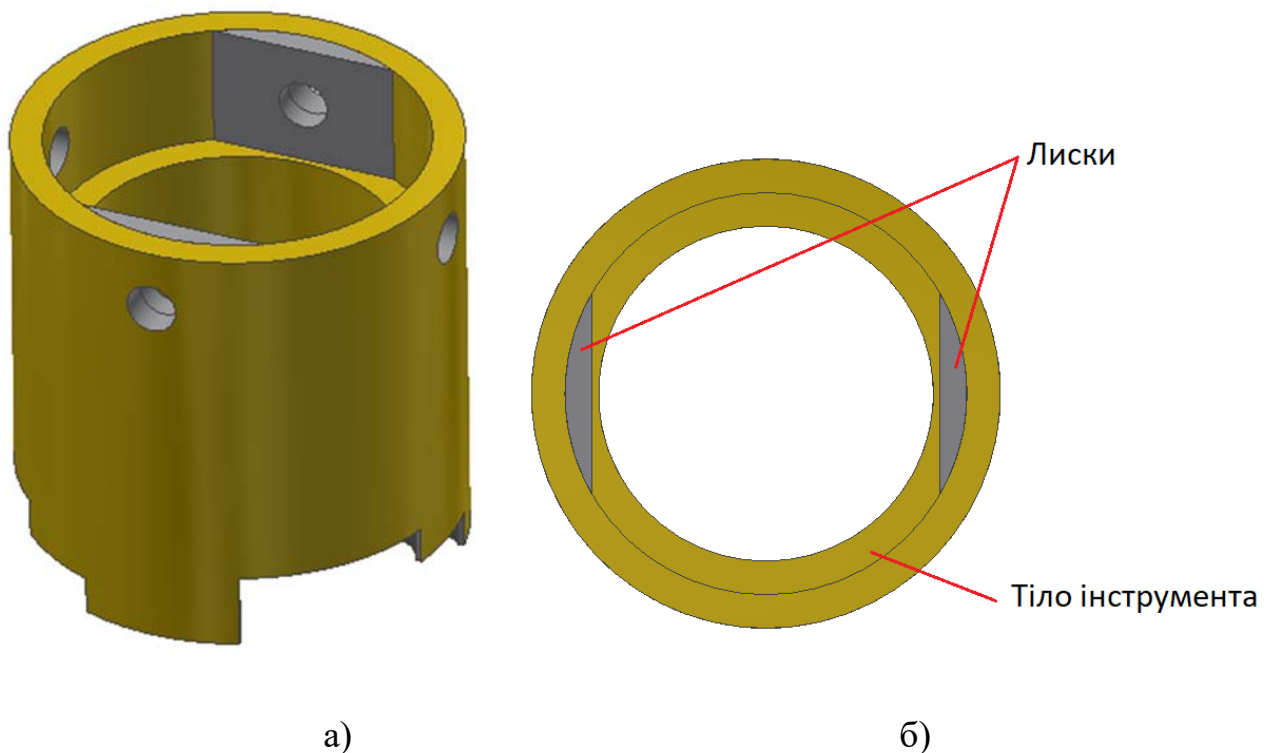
Лиски (а – аксонометрія, б – вид зверху)
